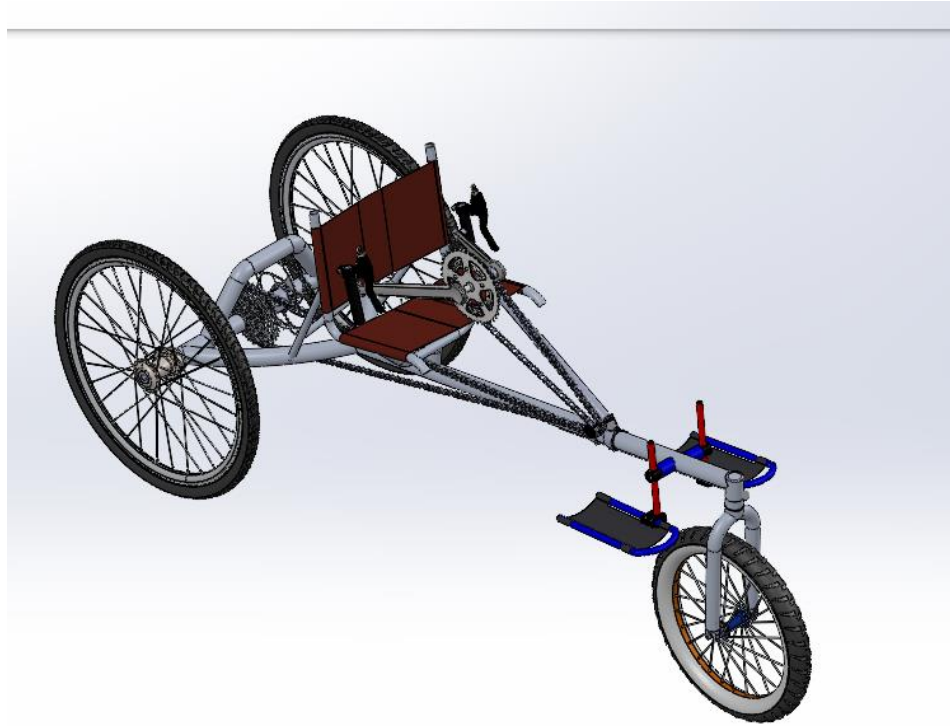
Ensamble final vista 3 hecho en SolidWorks.
